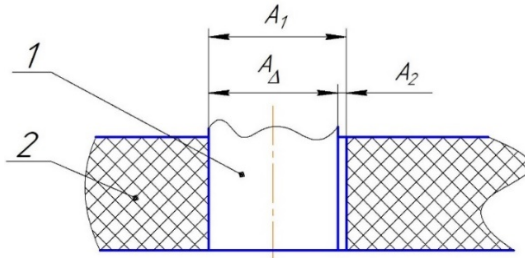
Схема размерного анализа получения отверстия под выталкиватель. 1 – выталкиватель; 2 – металлополимерная часть формообразующей детали пресс-формы; A_{Δ} – размер выталкивателя; A_1 – размер отверстия под выталкиватель; A_2 – величина усадки металлополимера.
